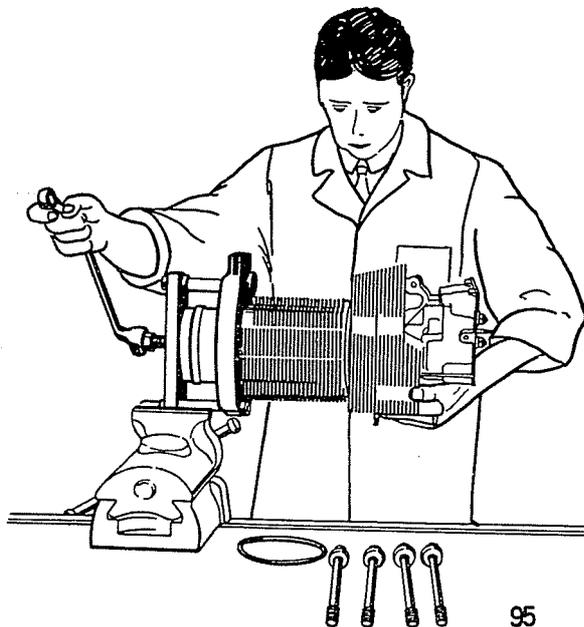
Abdrücken des Zylinderkopfes vom Zylinder früherer Ausführung
